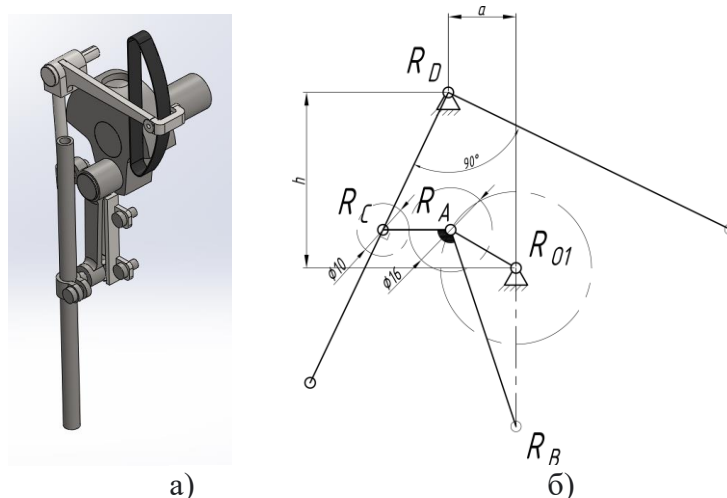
Механізм ниткопритягувача кулісного типу швейних машин загального призначення: а – 3D модель механізму в SolidWorks, б – кінематична схема механізму
